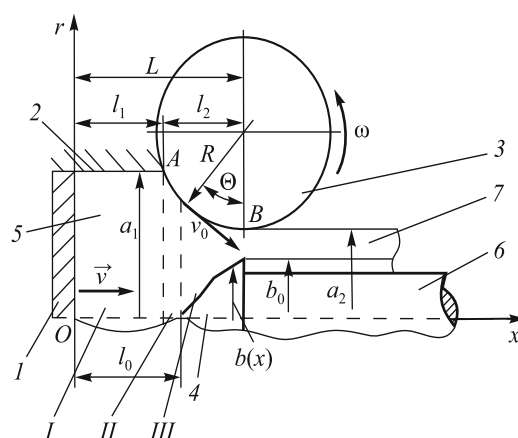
Расчетная схема процесса пресс-валковой прошивки трубной заготовки:
